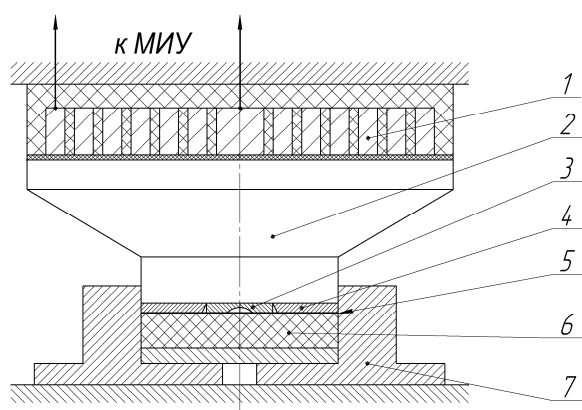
Технологическое устройство МЭИШ: 1 – спиральный индуктор, 2 – подвижный элемент, 3 – матрица для формовки и вырубки, 4 – вкладыш, 5 – заготовка, 6 – полиуретан, 7 – контейнер
